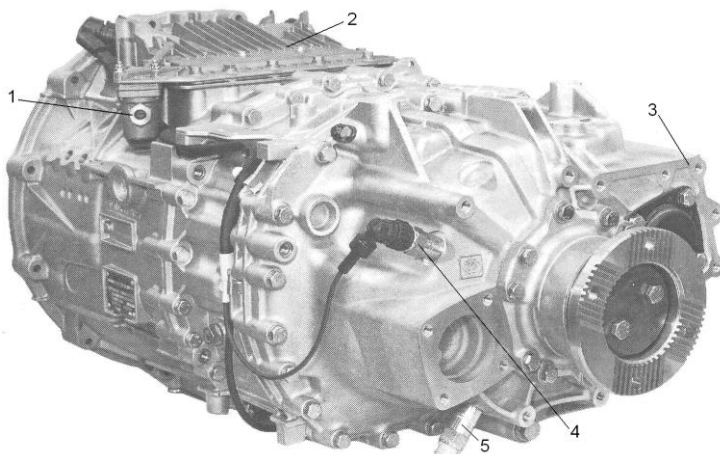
Общий вид автоматизированной коробки передач ZF 16AS2601:
